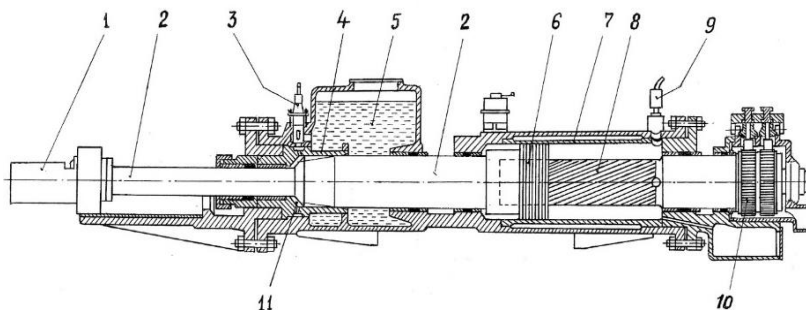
Форголлер подавального апарата з пневматичним розгоном і пневмогидравлічним гальмуванням рухомих частин: 1 – дорновий замок; 2 – шпиндель (шток); 3 – дросельний клапан; 4 – втулка гальмування; 5 – водяна камера; 6 – поршень; 7 – повітряний циліндр; 8 – дріль; 9 – електропневматичний клапан швидкого скидання і автоматичного заповнення; 10 – храповий механізм; 11 – камера гальмування
